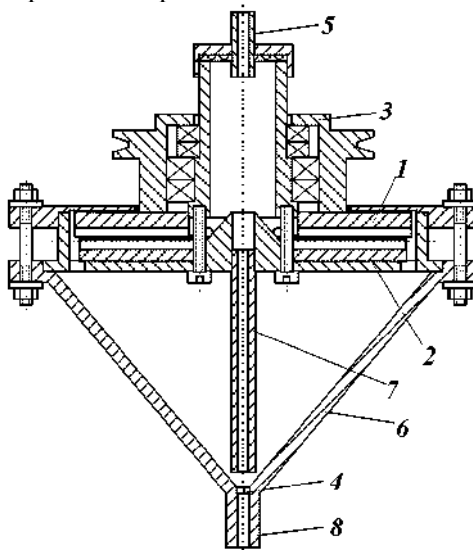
Роторный вихревой аппарат: 1 – ротор; 2 – статор; 3 – приводная головка; 4 – решетка; 5, 8 – патрубок; 6 – корпус; 7 – транспортирующая труба.
